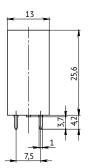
Габаритные, установочные, присоединительные размеры pene OptiRel G RP40-52 и OptiRel G RP40-61 с NO контактами
